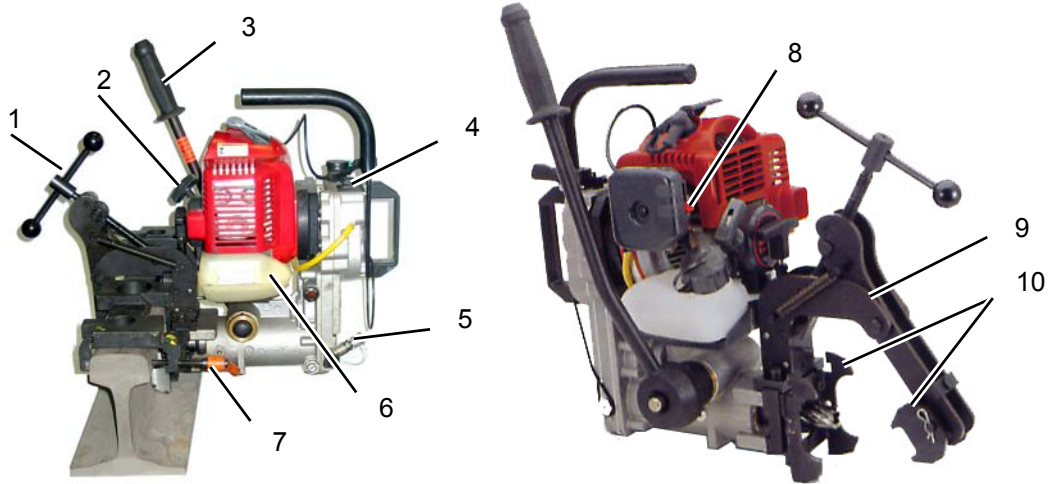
Übersicht Bohrvorrichtung LD-1P mit Befestigungsarm
